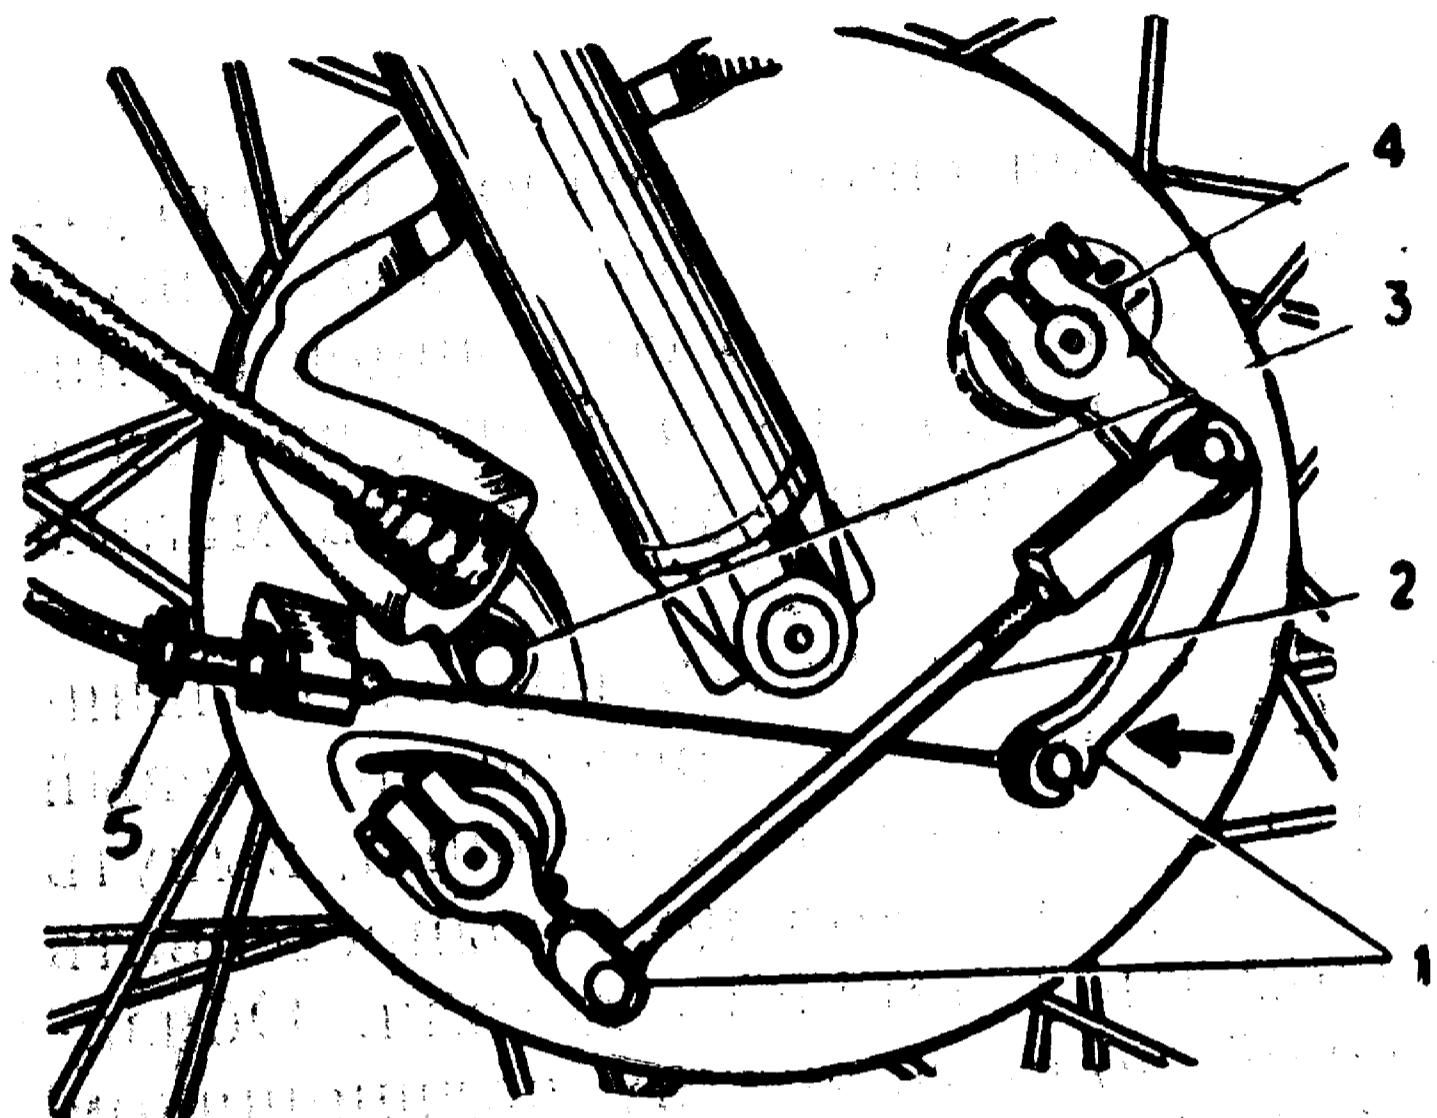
Снятие переднего колеса с двухкулачковым тормозом:
